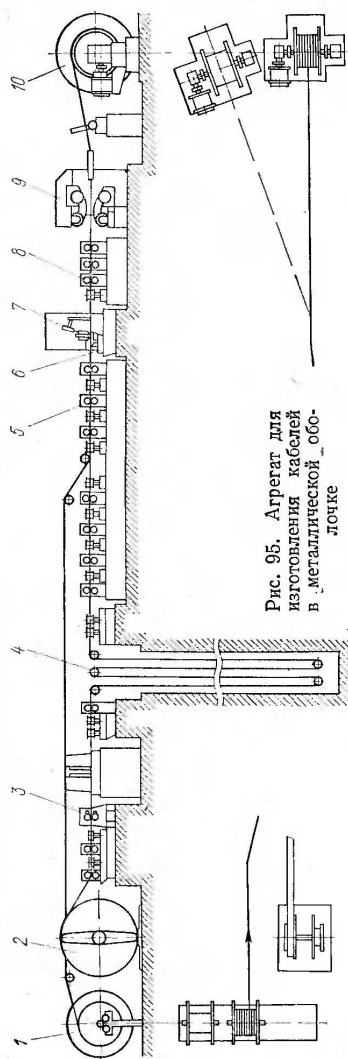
Агрегат для изготовления кабелей в металлической оболочке
